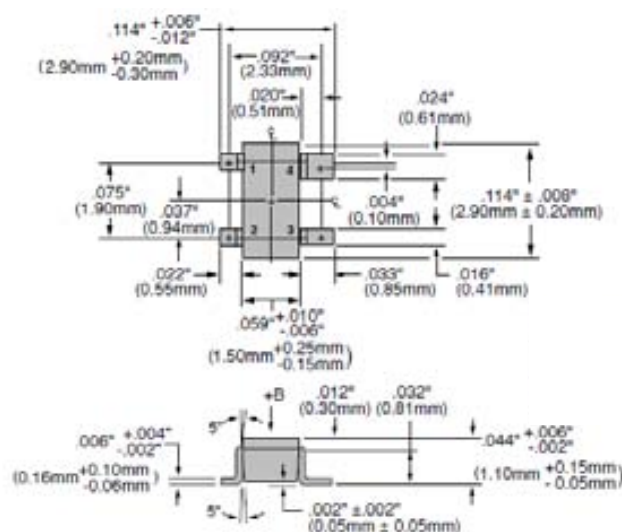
Dimensions dels sensors Hall GH-700 usats en aquesta tesi.
